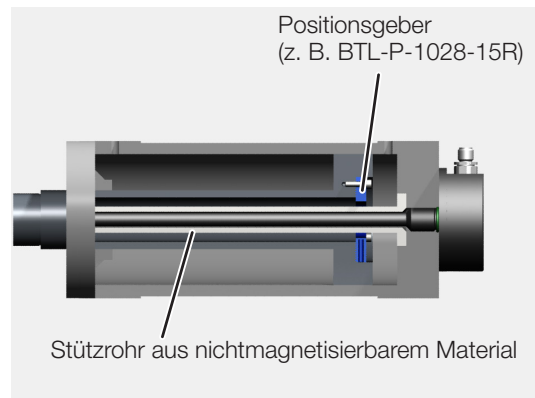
Beispiel 2, BTL wird mit Stützrohr eingebaut
